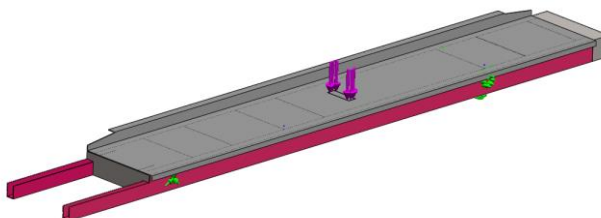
Расчетная схема верхней платформы (Вариант 1)
